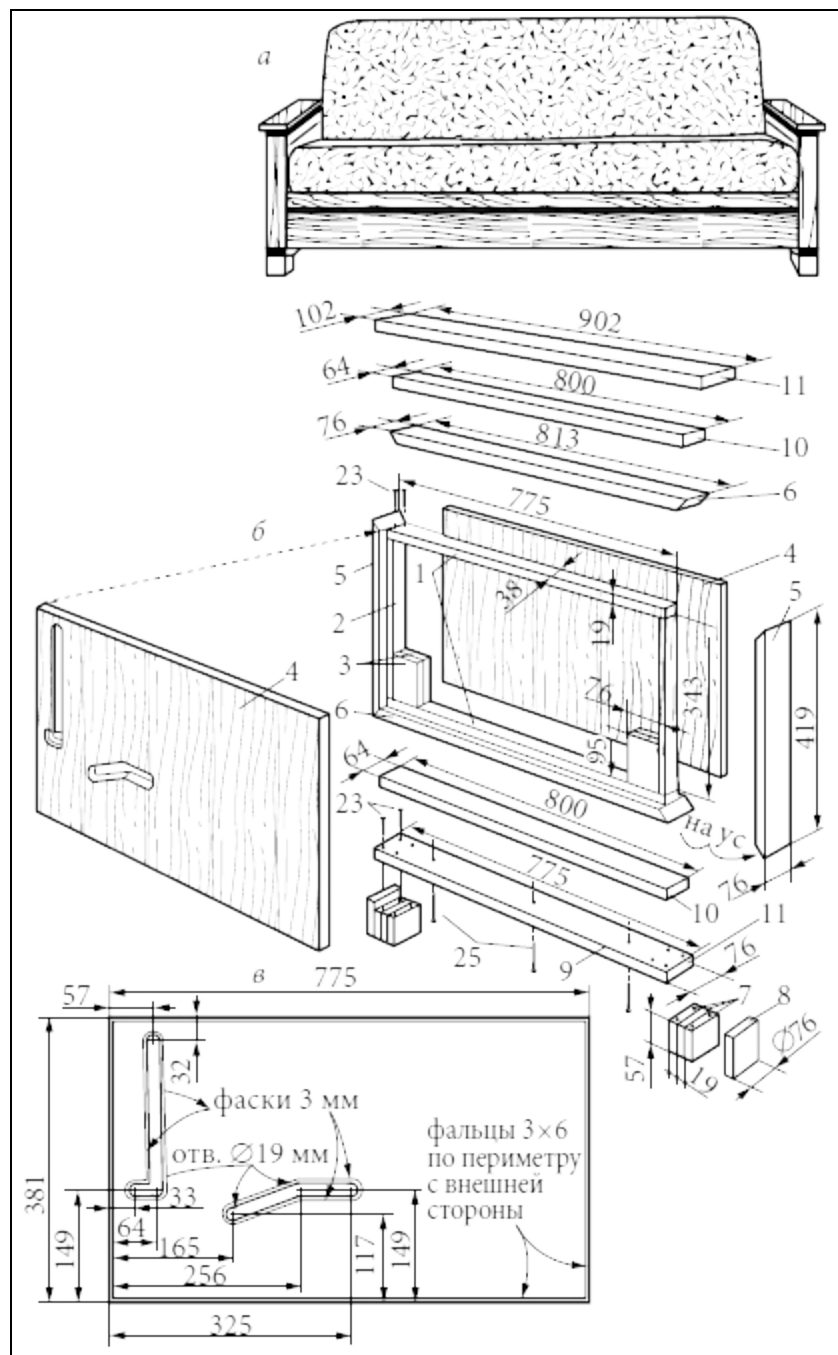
Диван-кровать. Общий вид и сборка боковин^[6]:
